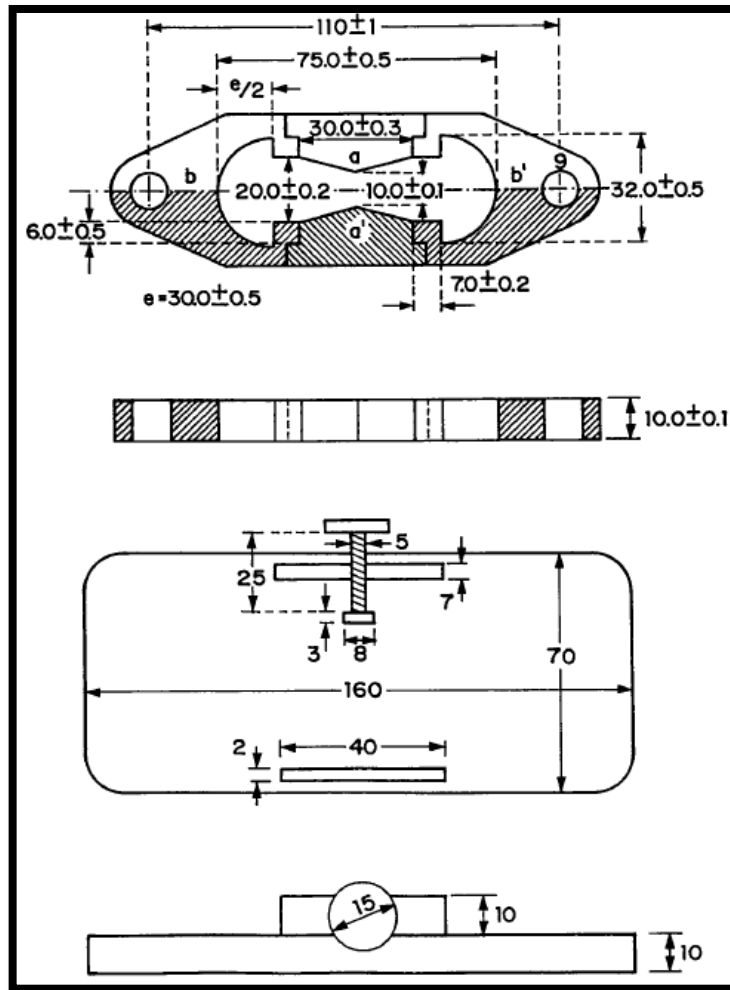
MOLDE Y PLACA PARA DUCTILÓMETRO
